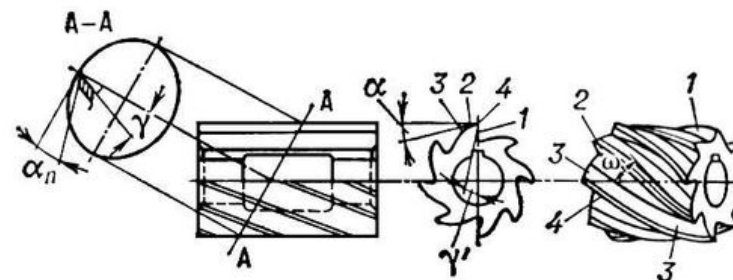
Геометрические параметры режущей части цилиндрической фрезы:
